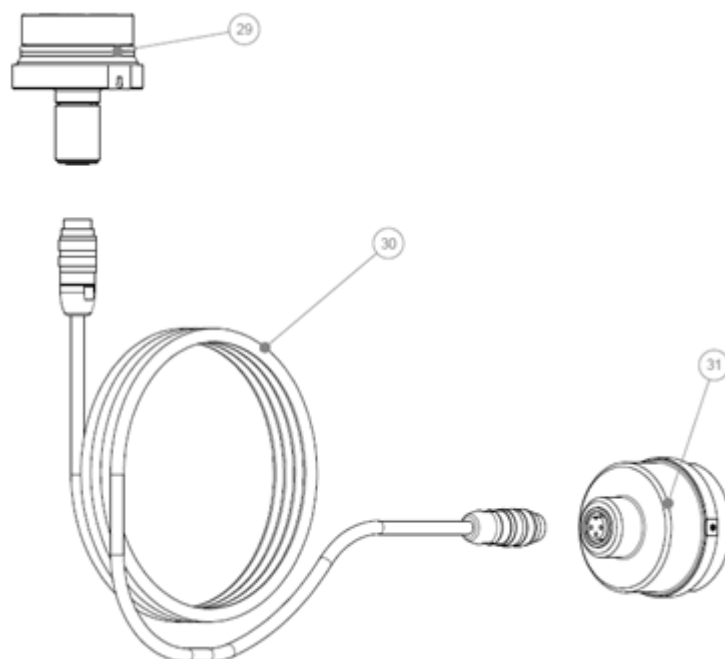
Desenho explodido do sensor remoto do VTP10-H.
